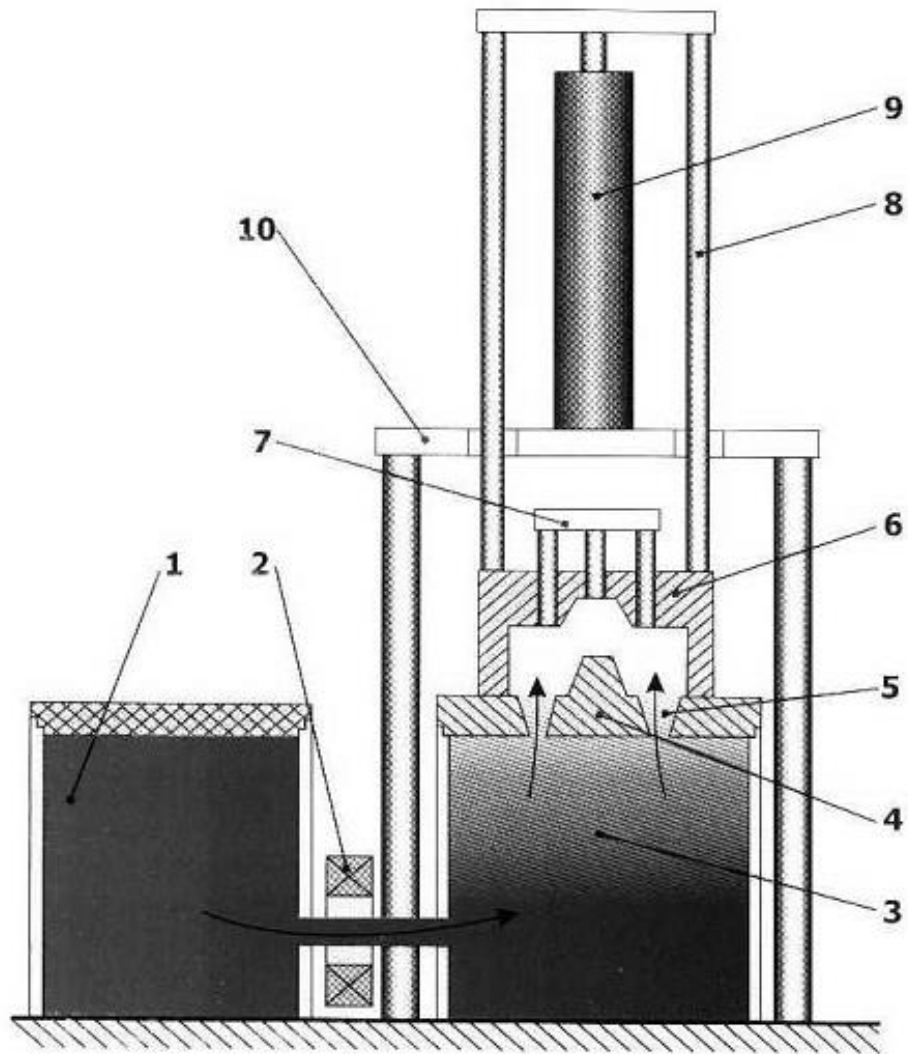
Схема лабораторної установки “РОЗЛИВ-ЛЕМТ”
